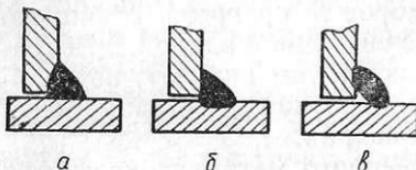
Различные случаи несплавления в сварных швах таврового соединения:
